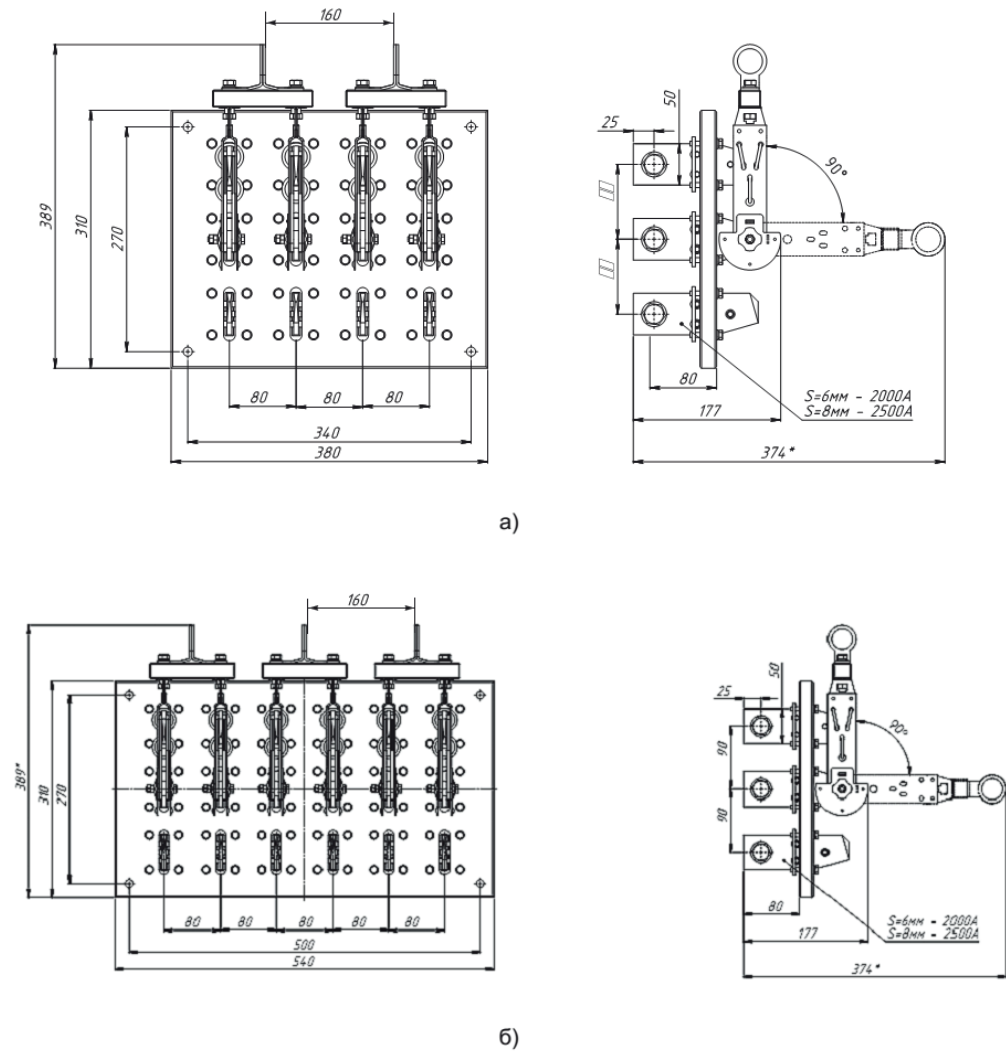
Разъединитель РЕ19 на два направления с центральной рукояткой
